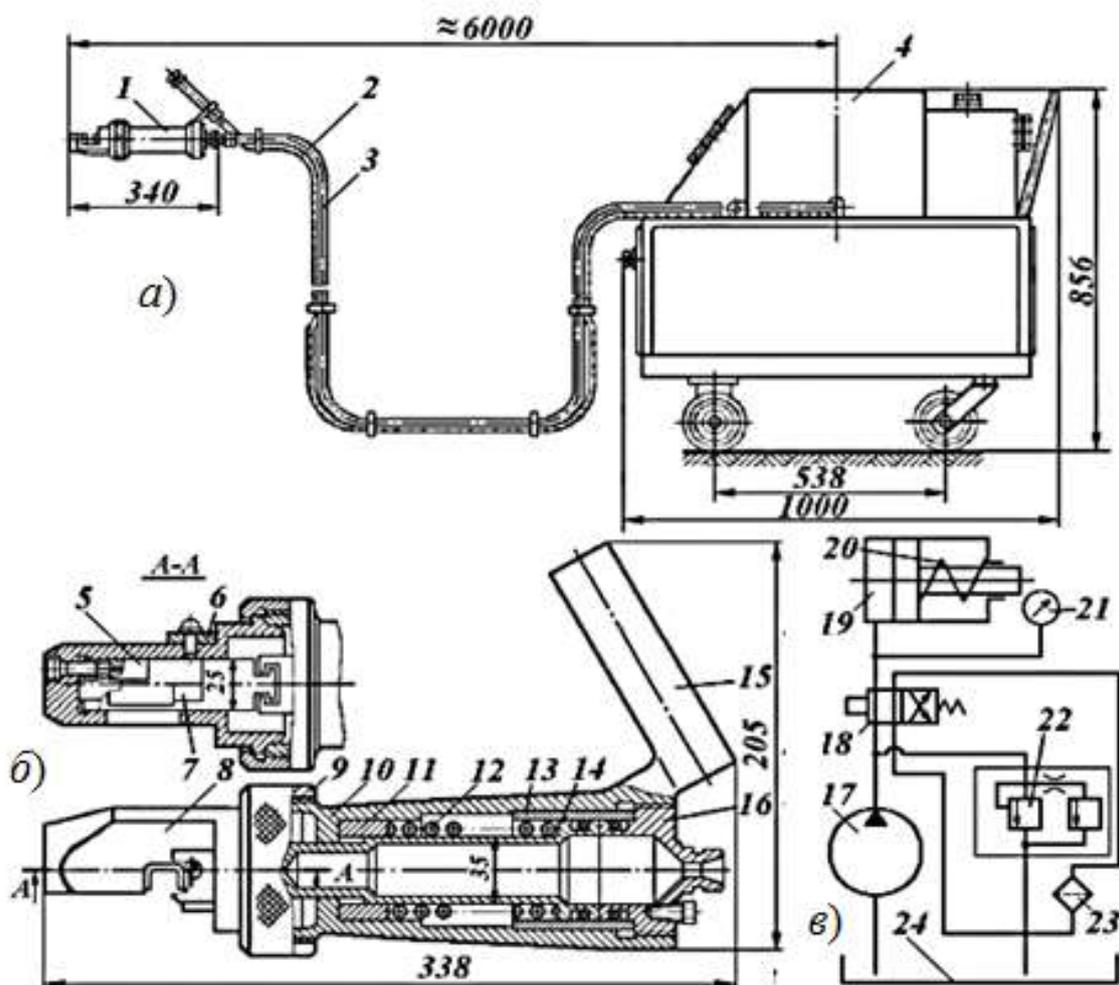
Ножницы СМЖ-214А: а – общий вид; б – режущая головка; в – гидросхема; 1 – режущая головка; 2 – электрокабель управления; 3 – рукав высокого давления; 4 – насосная установка; 5, 7 – неподвижный и подвижный ножи; 6 – опорная планка для стержня; 8 – ножевая головка; 9, 16 – передняя и задняя крышки; 10 – корпус; 11, 13 – втулки; 12 – пружина; 14 – поршень; 15 – рукоятка; 17 – эксцентриковый поршневой гидронасос; 18 – гидрораспределитель; 19 – гидроцилиндр; 20 – пружина; 21 – манометр; 22 – предохранительный клапан; 23 – сетчатый фильтр; 24 – гидробак.
